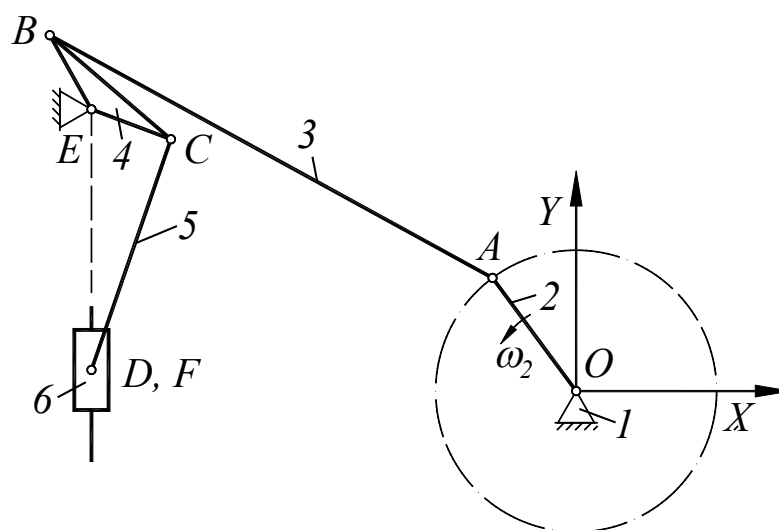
Кинематическая схема механизма штамповочного прессы
